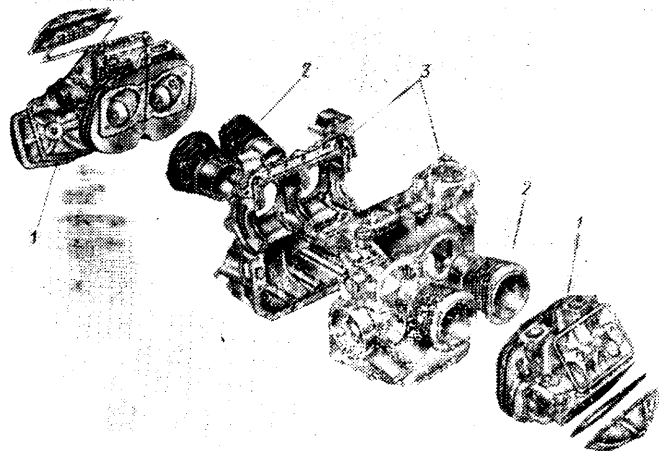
Общий вид и компоновка блока двигателя: 1 — головка цилиндров; 2 — цилиндры; 3 — полукорпусы
